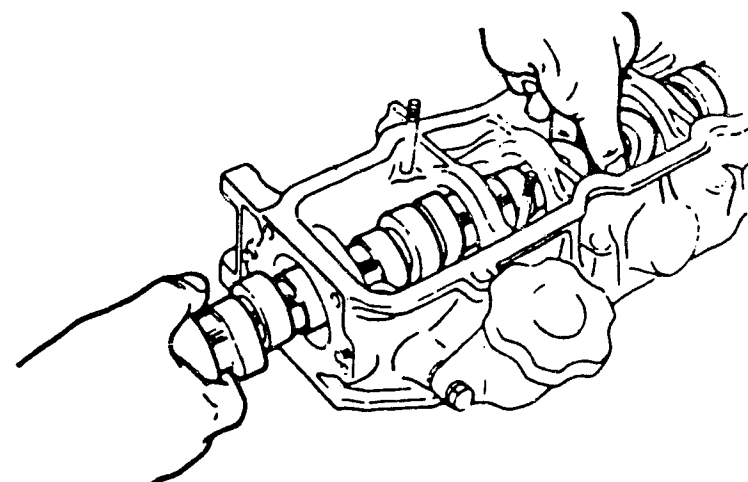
Motor 1S: Während die Nockenwelle langsam gedreht wird, lässt sie sich aus dem Gehäuse ziehen.
